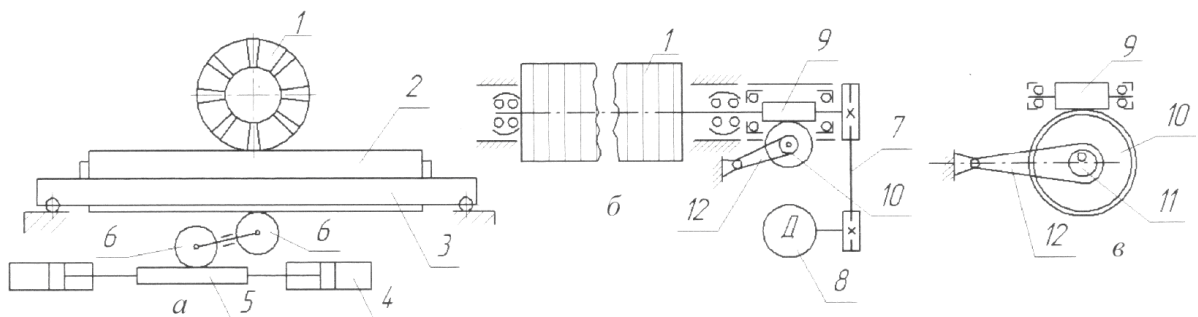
Гідрокінематична схема полірувального верстата ПІБ: а - привод каретки; б - привод полірувального барабана; в - механізм осциляції; 1 - полірувальний барабан; 2 - деталь; 3 - каретка; 4 - гідроциліндри; 5 - рейка; 6 - зубчасті колеса; 7 - клинопасова передача; 8 - електродвигун; 9 - черв'як; 10 - черв'ячне колесо; 11 - ексцентрик; 12 - шатун
